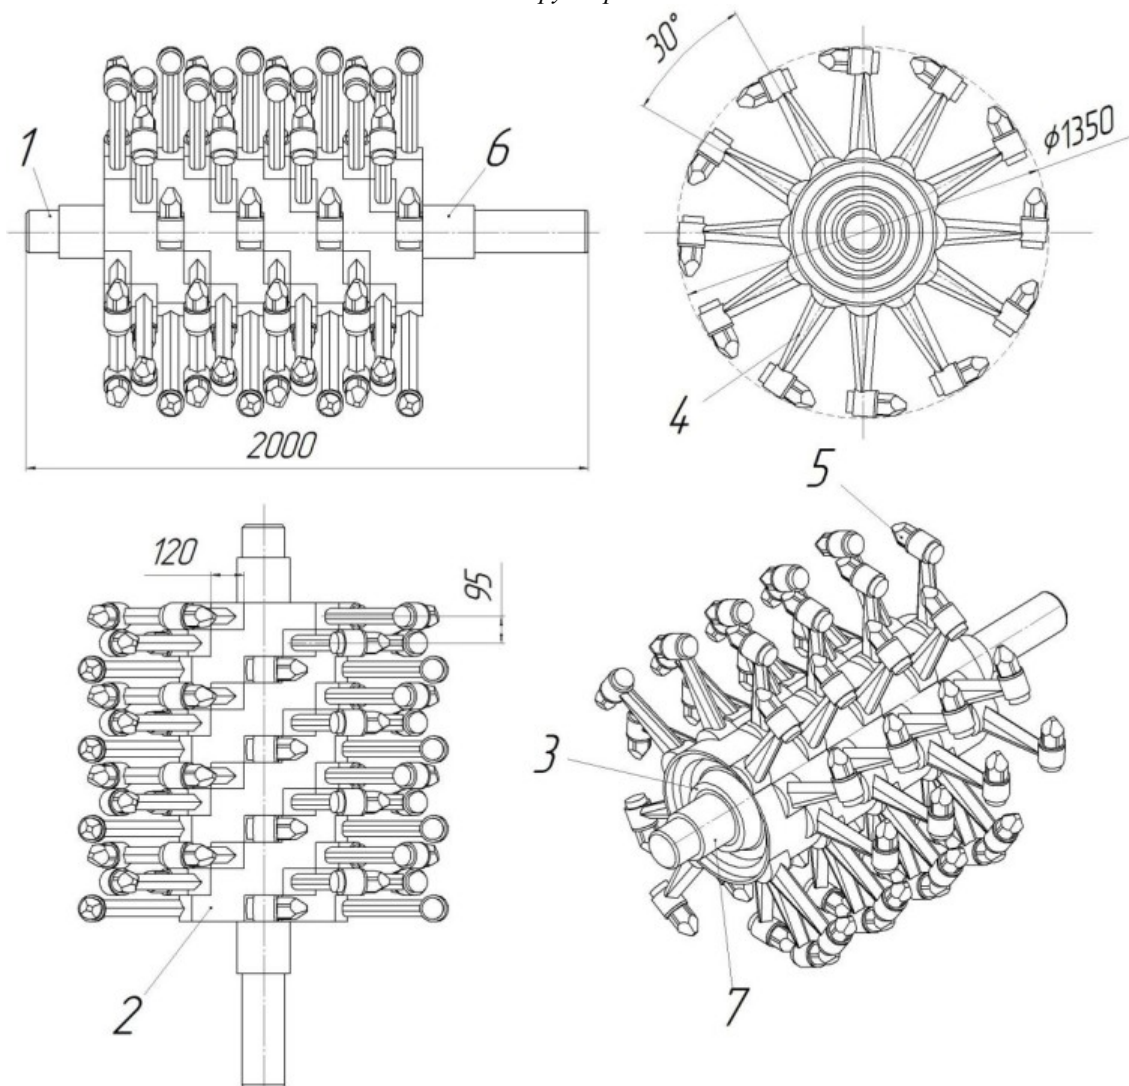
Загальний вигляд робочого органу машини для руйнування дорожніх покриттів: 1 – вал; 2 – барабан; 3 – вкладки; 4 – стійка; 5 – різальний зуб, 6, 7 - втулка.
